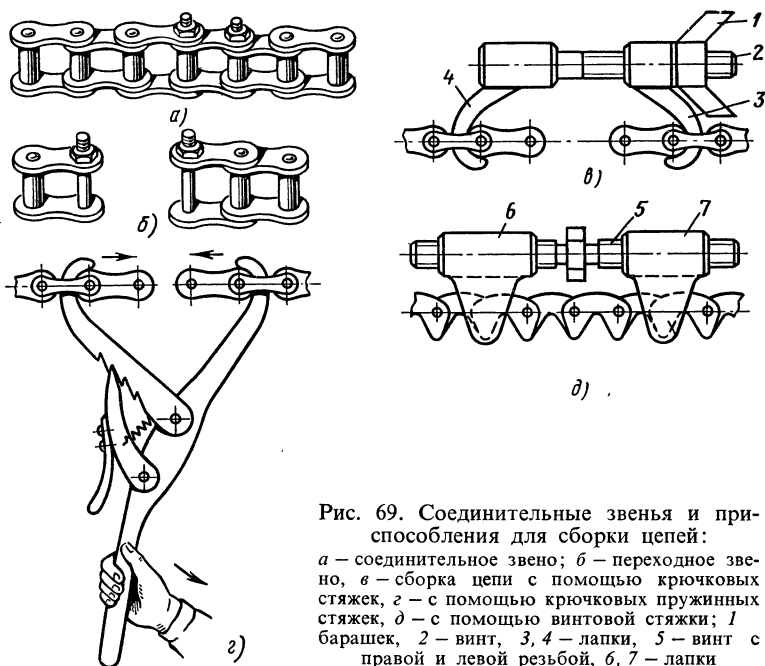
Соединительные звенья и приспособления для сборки цепей:
